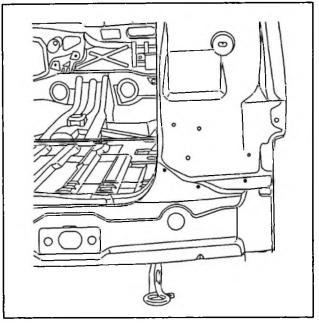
BP02UC Souder par points "bouchon" MAG. Meuler les points de soudure MAG.
